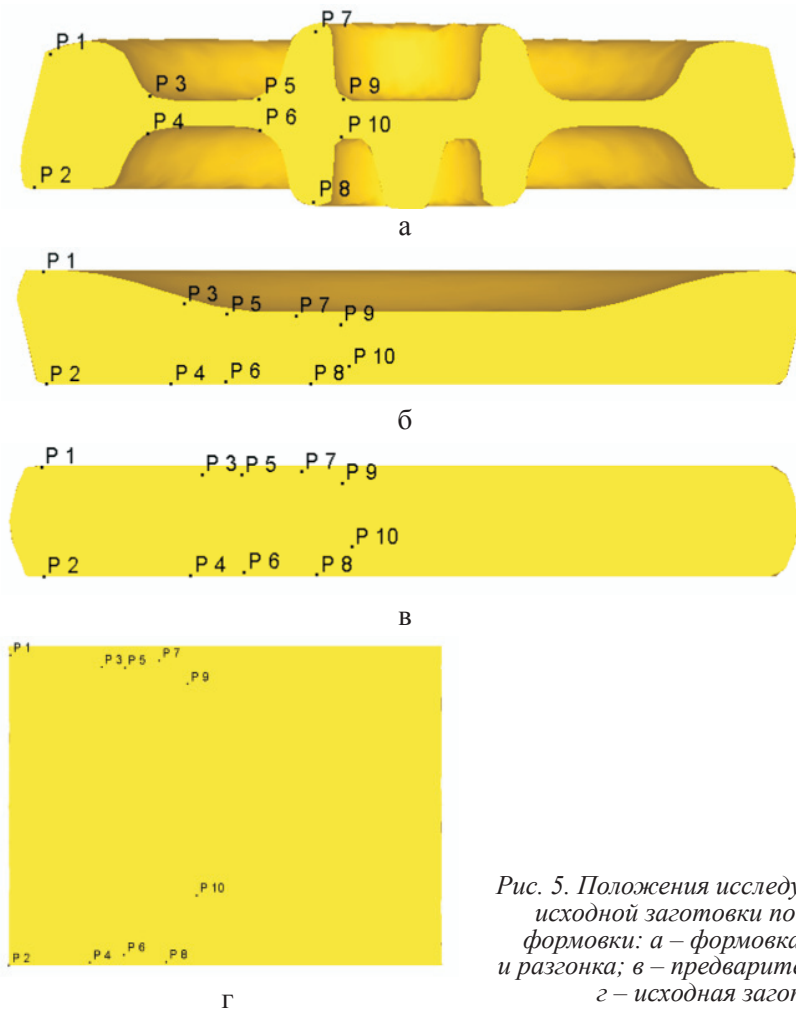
Положения исследуемых объемов исходной заготовки по переходам формовки: а – формовка; б – осадка и разгонка; в – предварительная осадка; г – исходная заготовка
